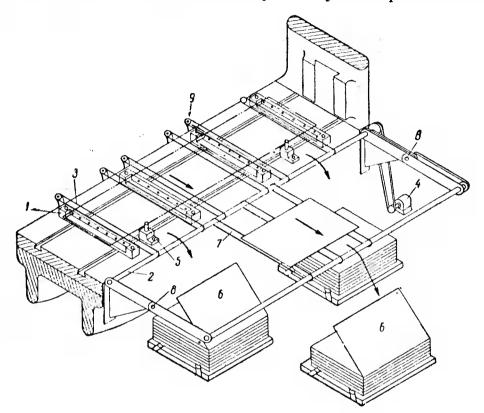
Одновременная резка нескольких заготовок на кривошипном прессе.
